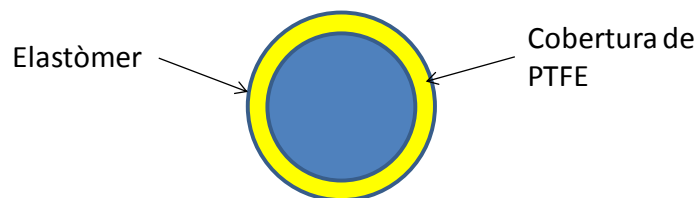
Secció transversal d'una junta tòrica encapsulada
